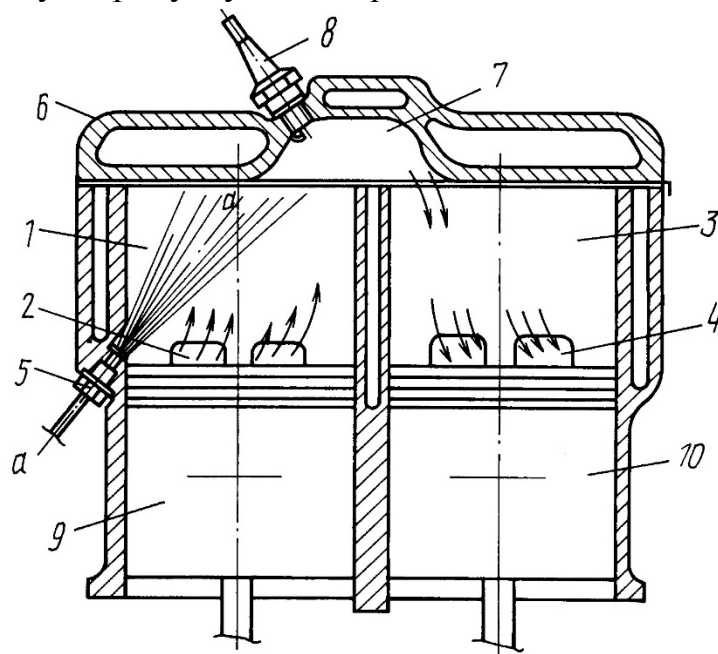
Двухтактные двигатели со средствами для распределения топливного заряда в цилиндрах слоями [6]: 1,3 – полости цилиндра; 2 – продувочные окна; 4 – выпускные окна; 5 – форсунка; 6 - поверхность головки цилиндра; 7 – камера сгорания; 8 – свеча зажигания; 9,10 – поршни.
